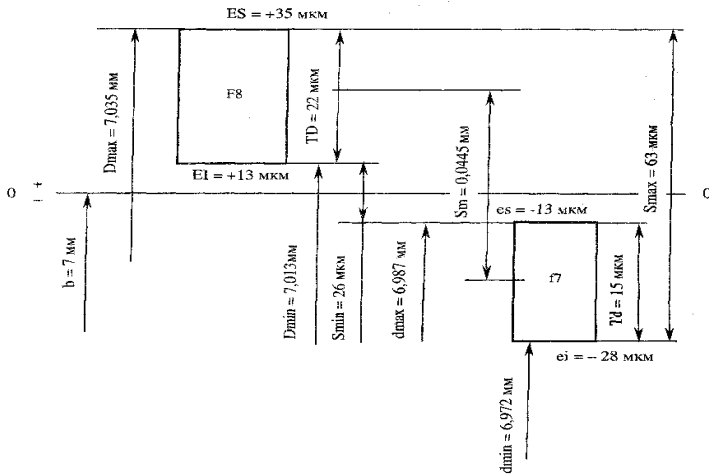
Схема розташування полів допусків для бічної поверхні b прямокутного шліцевого з'єднання.
